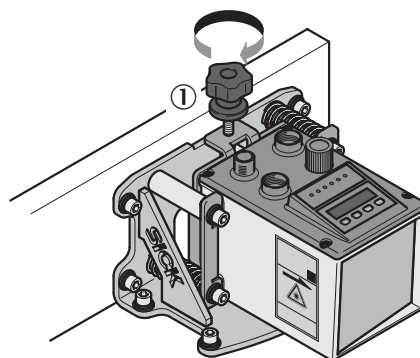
Entfernungs-Messgerät mit Rändelschraube befestigen
